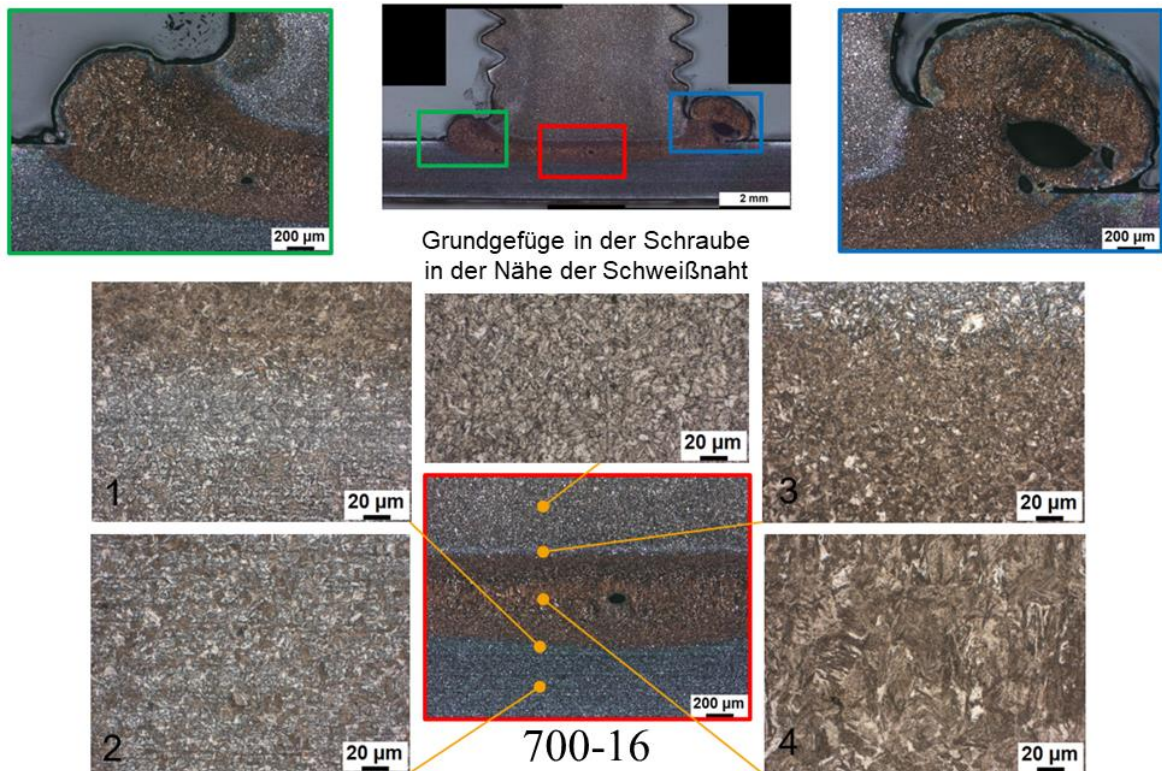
Mikrostruktur und lokale Geometrie der Schweißnaht der Bolzenprobe 700-16
